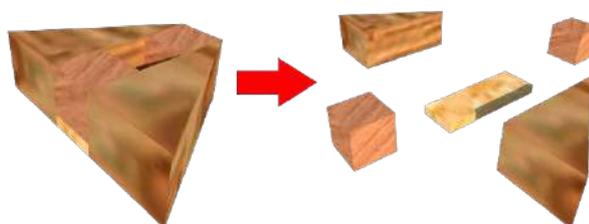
Móvel Sonobe, encaixes da base triangular. Vista tridimensional.
